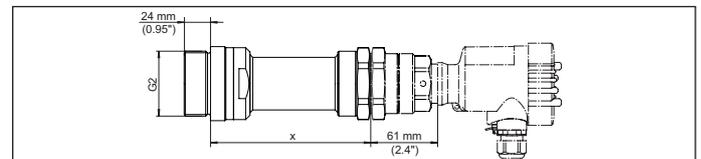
Montageadapter mit Keramikabdeckung (optional) für VEGAMIP mit innenliegender Hornantenne, Gewindeausführung G1½ mit PTFE-Abdeckung (auch mit 1½ NPT-Gewinde)
